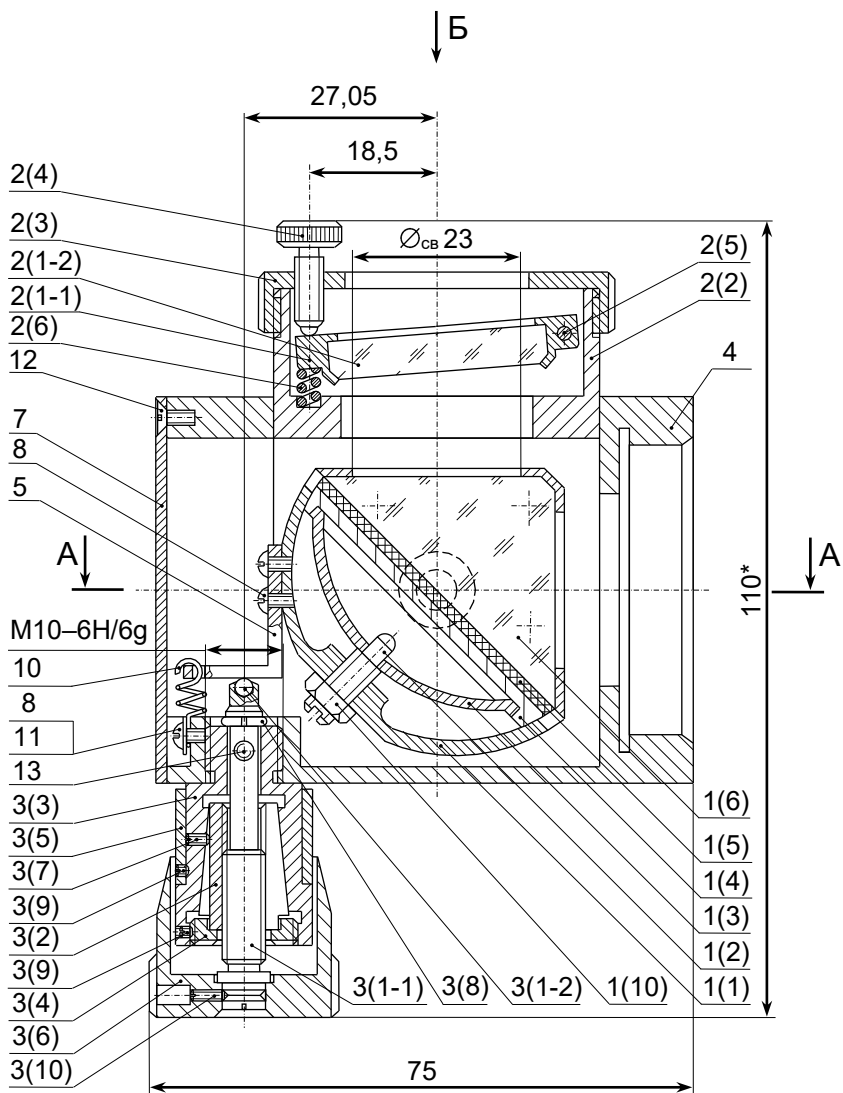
Конструкция механизма юстировки и крепления призмы АР-90° (главный вид)
